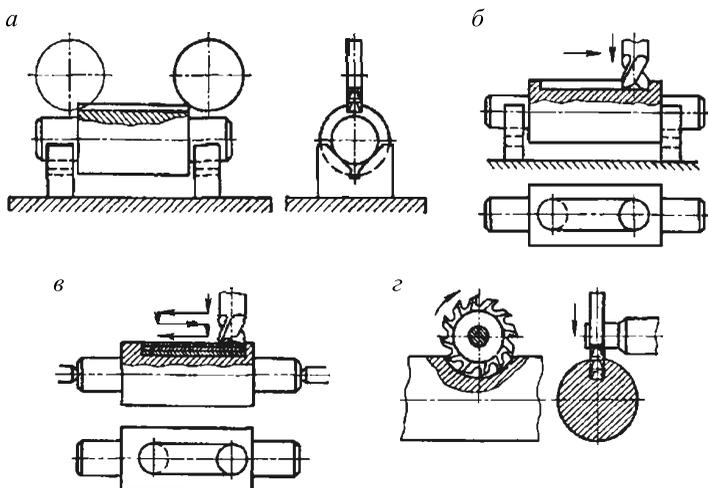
Схемы фрезерования шпоночных канавок валов
